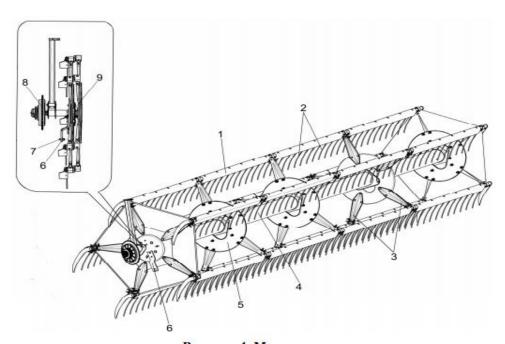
Мотовило; 1 — граблина; 2 — зуб пружинный; 3 — луч; 4 — вал мотовила; 5 — диск; 6 — поводок; 7 — ролик; 8 — приводная звездочка с предохранительной муфтой; 9 — эксцентриковый механизм.
